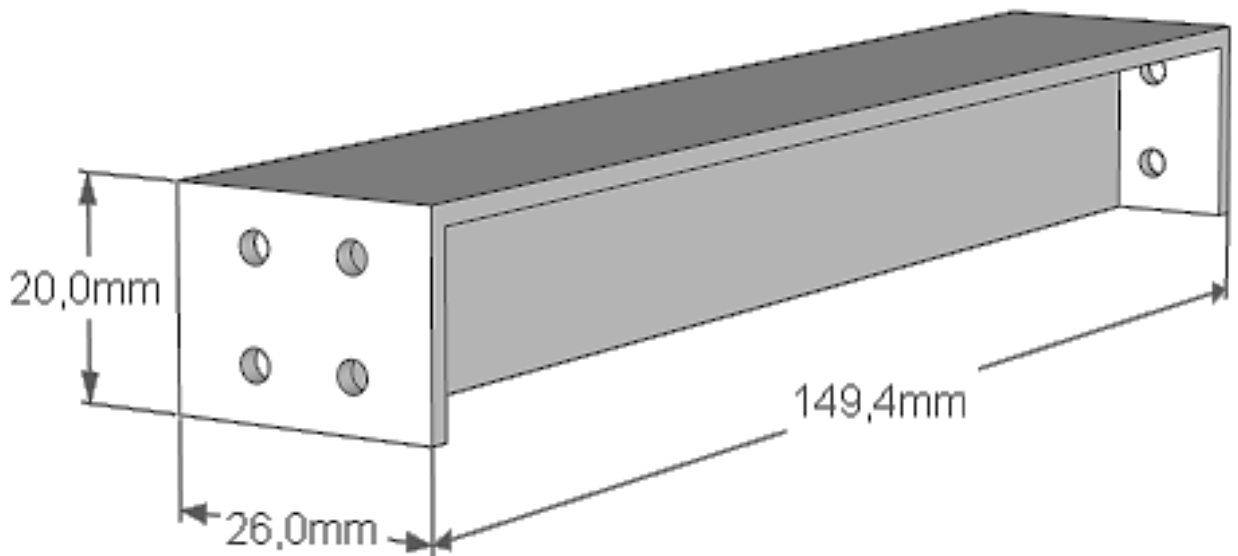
3D-модель другої ланки з позначеними габаритними розмірами.
